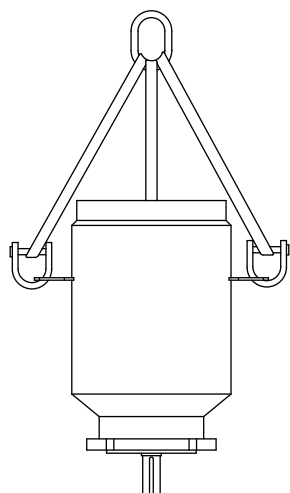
Esempio: sollevamento corretto del motore con occhielli di sollevamento
